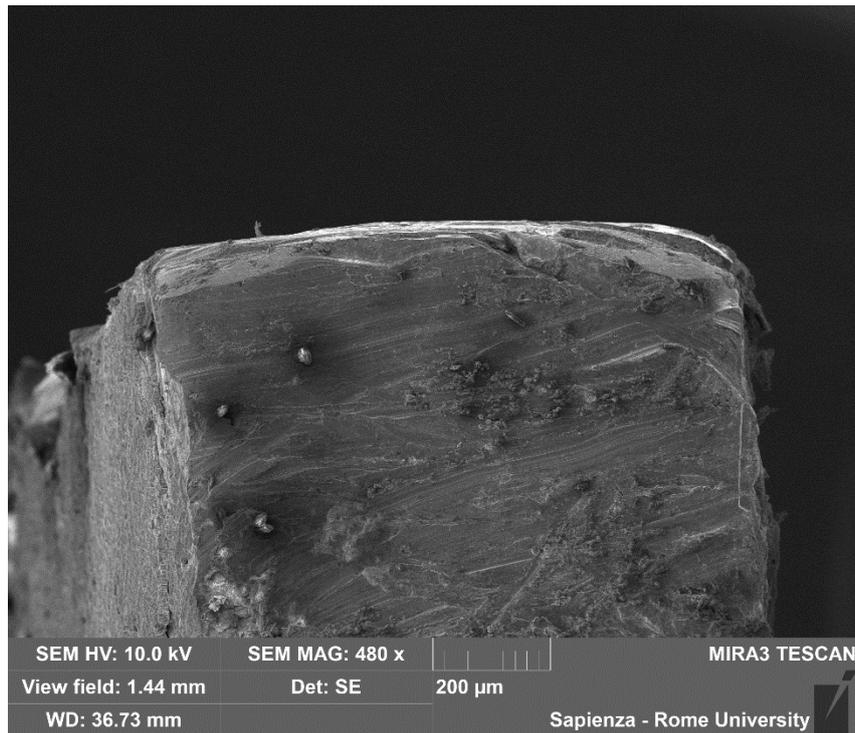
schiacciamenti della superficie di rottura denominata 1 (foto 17) dell'occhiello.
